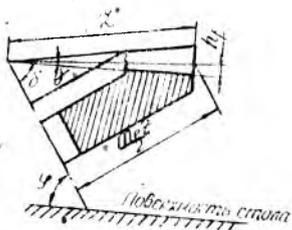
Схема установки заготовки конического колеса при фрезеровании впадин зуба
